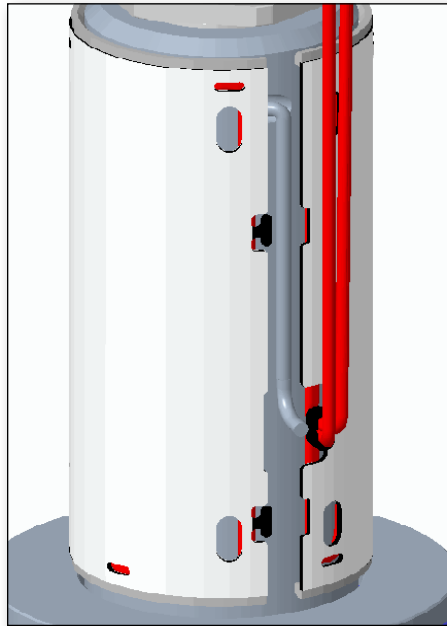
Conjunto de tubo y manga de calentador instalado
